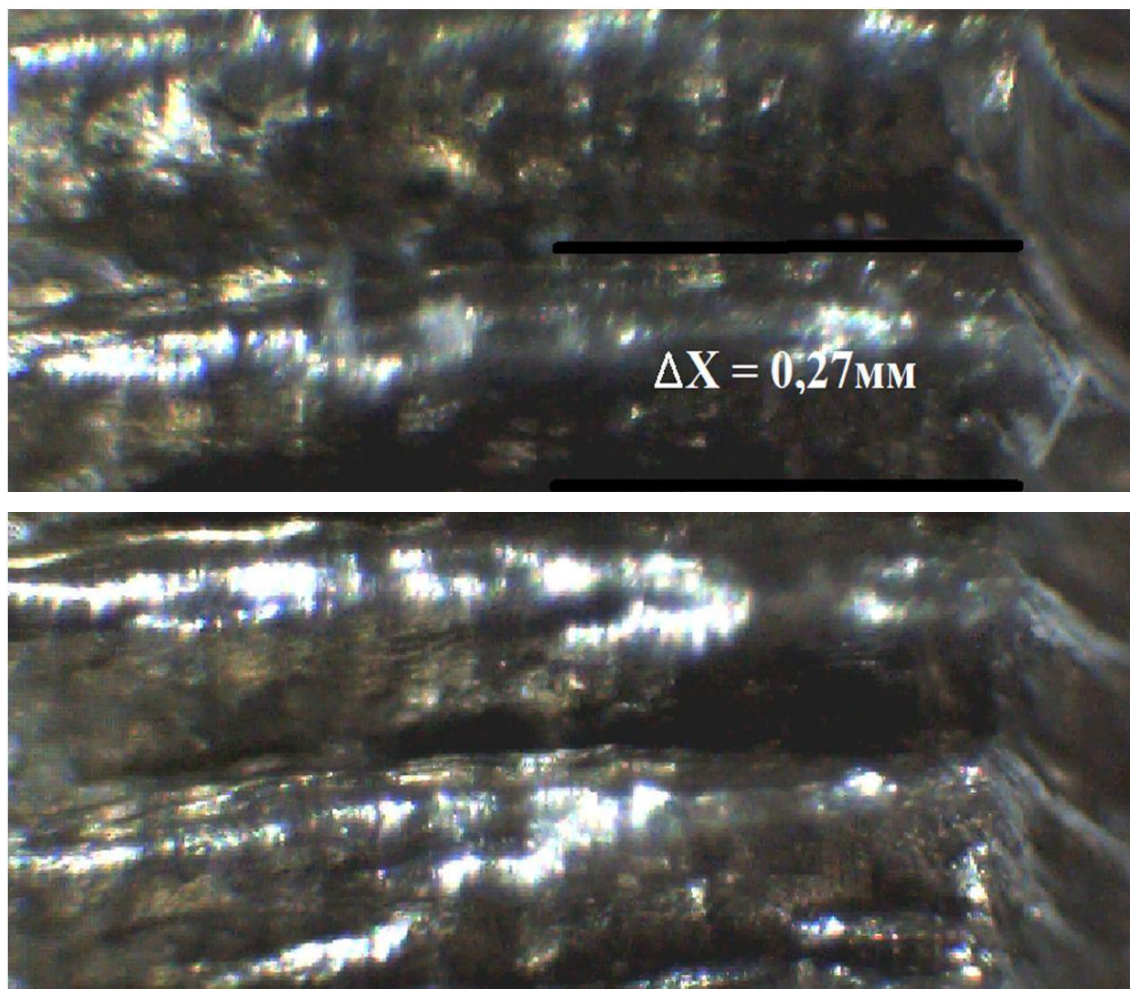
Увеличенное фото стружки.. Сталь 12X18H9Т. Режущий инструмент с твердосплавными режущими пластинами. Продольная подача 0.31 мм/об.,
